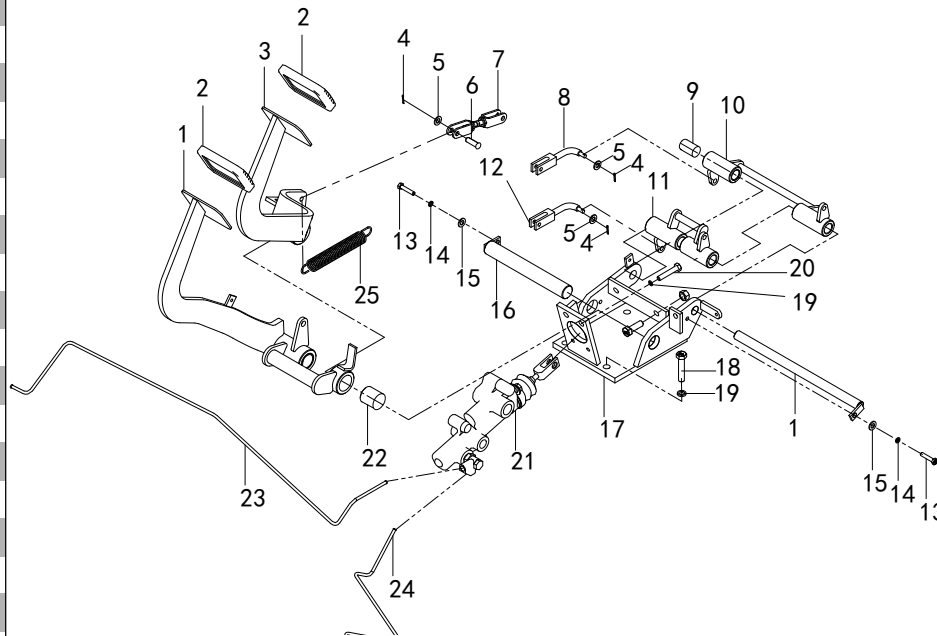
行车制动与微动操纵 (锡柴 4DX23 发动机)		BRAKE & INCHING CONTROL (4DX23)
